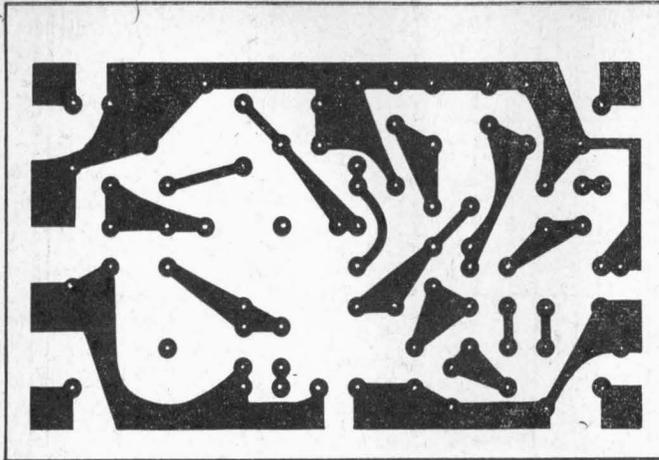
Plaqueta de circuito impresso para montagem do receptor da Fig. 1. Dimensões: 57 x 87 mm.
